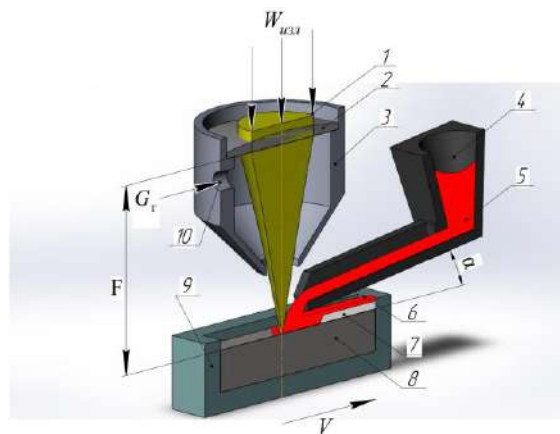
Схема получения биметаллической конструкции под действием лазерного излучения, где: 1 – лазерное излучение, 2 – фокусирующий элемент, 3 – сопло, 4 – дозирующий лоток, 5 – расплав металла, 6 – затвердевающий слой, 7 – залитый слой, 8 – заготовка, 9 – ограничители, 10 – защитный газ.
